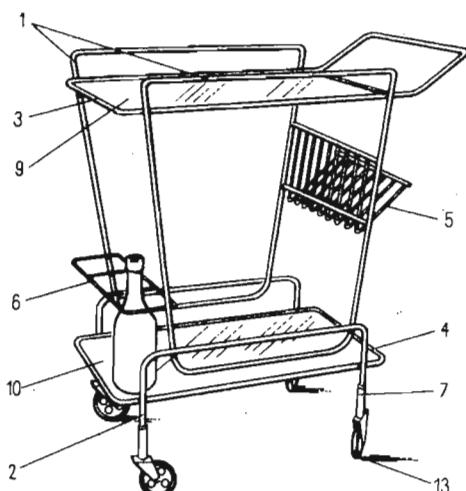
Сервировочный столик трубчатой конструкции
